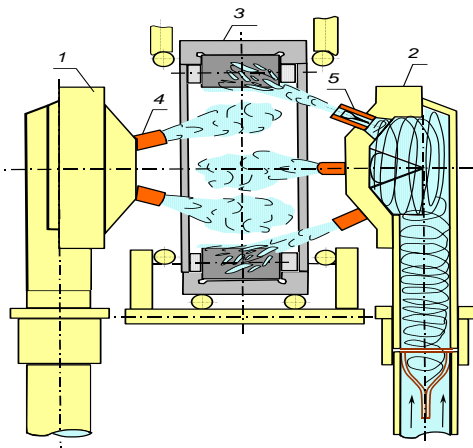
Устройство для промывки буксовых подшипников: 1, 2 – струйно - кавитационные головки; 3 – промываемый подшипник; 4 – сопла; 5 – кавитатор.
